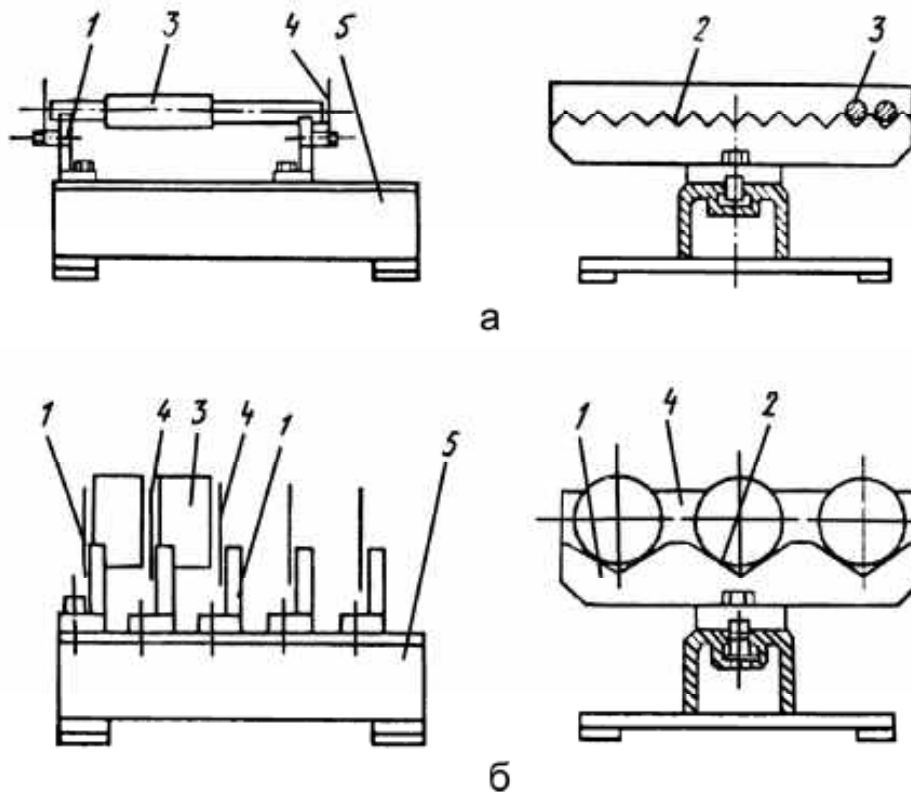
Схема магазинів для деталей типу тіл обертання:
